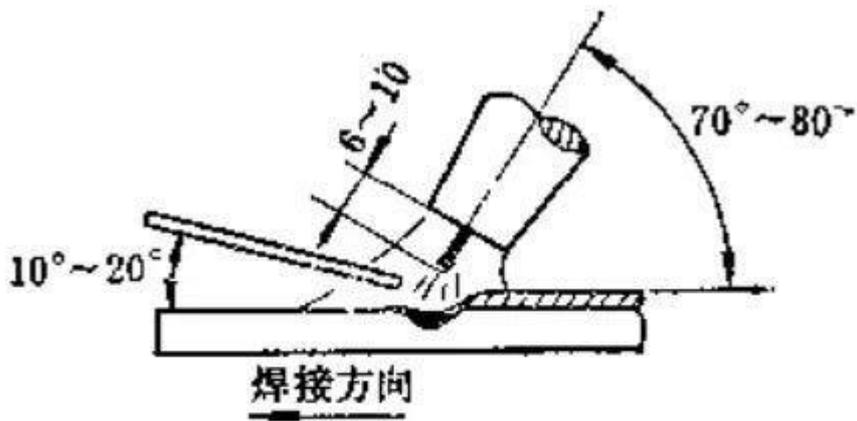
钨极手工氩弧焊时，焊炬、焊丝与焊件间的角度 焊接互联
